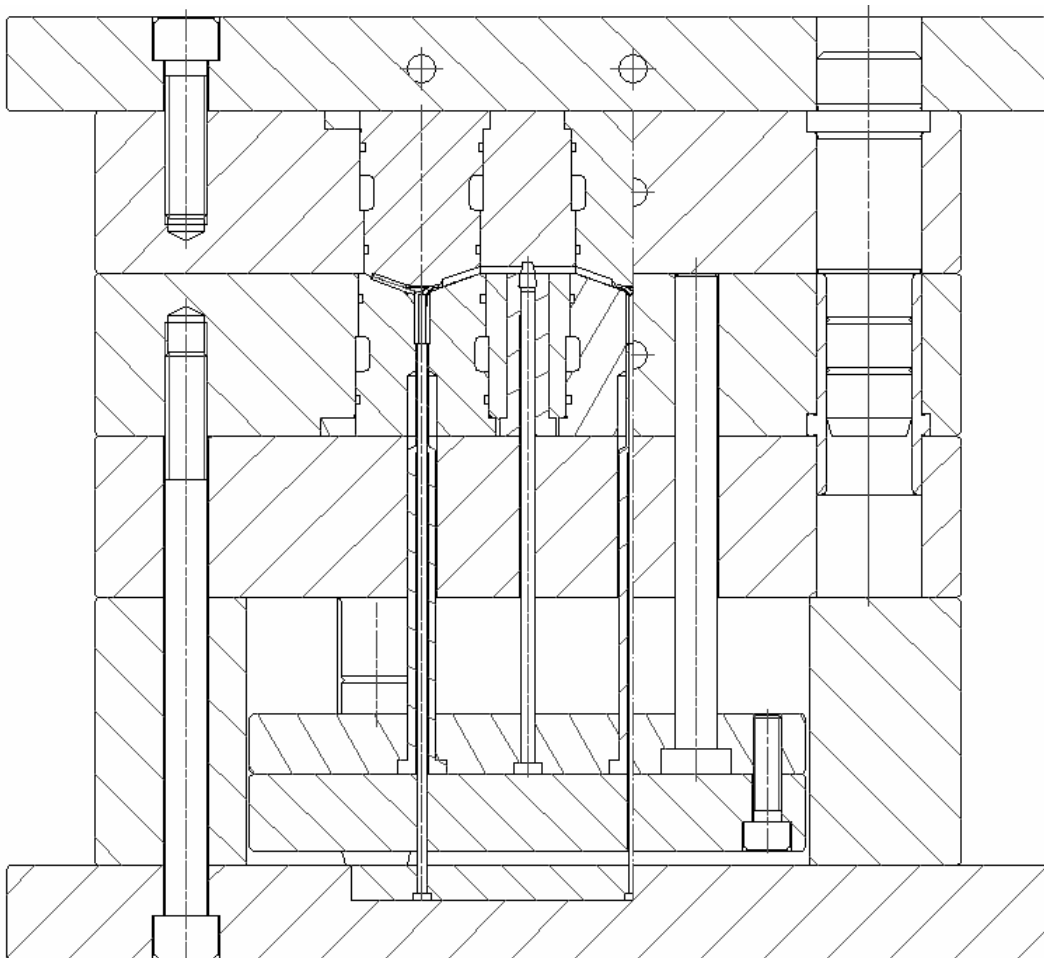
Molde para injetar a unidade representativa do carbono-alfa: Desenho técnico em corte da montagem
